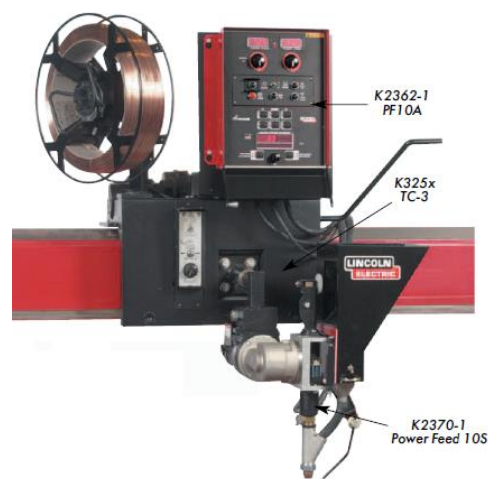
Оборудование для сварки под слоем флюса
